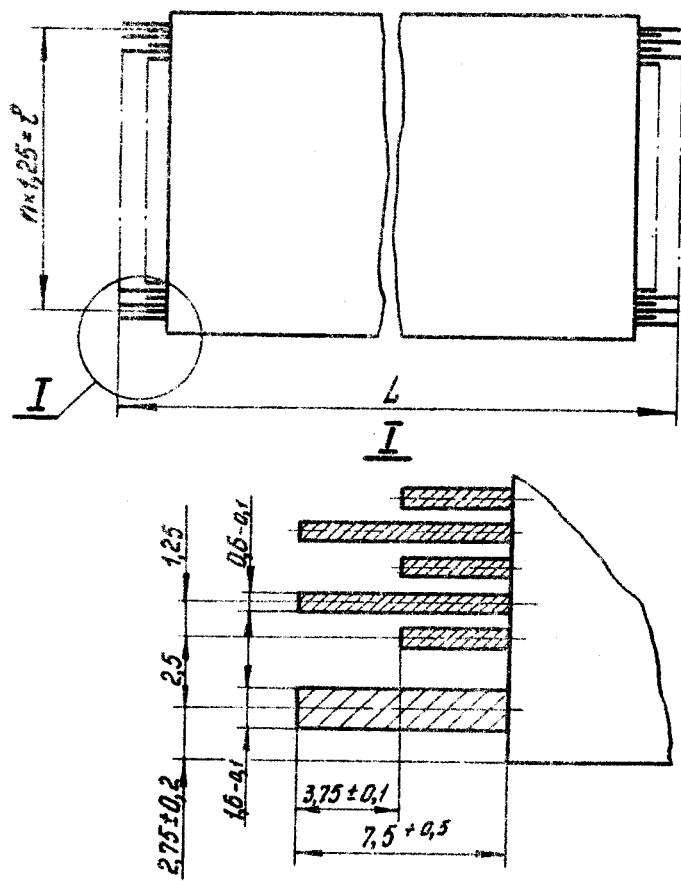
Гибкий печатный кабель с двухрядными контактными лепестками.
